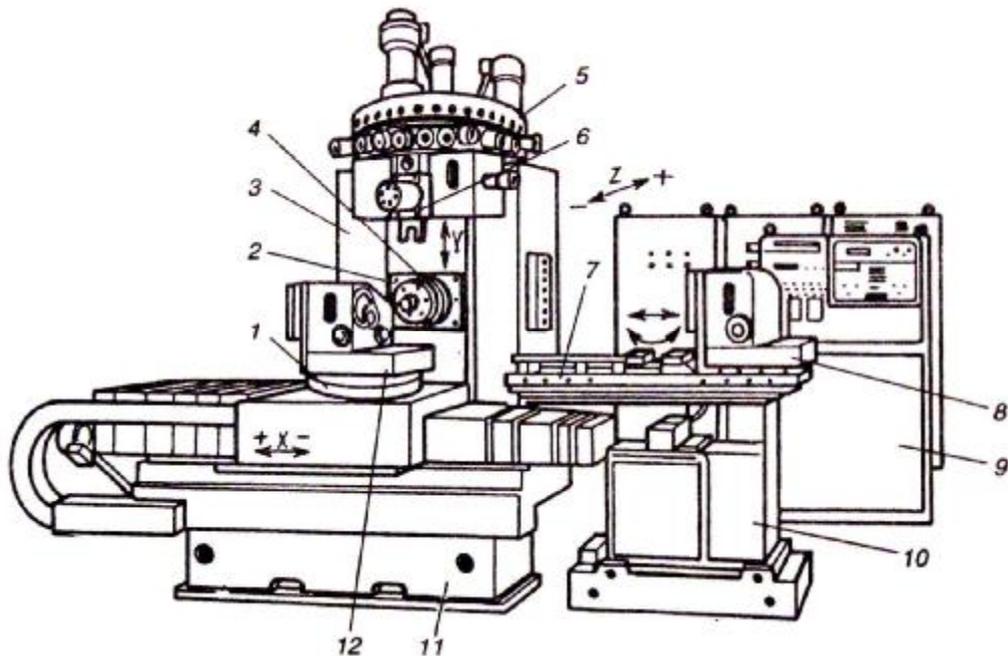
Многоцелевой станок сверлильно-фрезерно-расточный ИР500МФ4: *1* – стол поворотный; *2* – бабка шпиндельная; *3* – стойка; *4* – шпиндель; *5* –магазин инструментов; *б* – автооператор двухзахватный; *7* – стол двухпозиционный; *8* – спутник (на загрузке); *9* – УЧПУ; *10* – станина дополнительная; *11* – станина; *12* – спутник (под обработкой)
